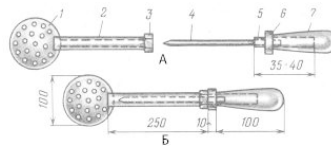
Черпак-пешня: 1 – черпак; 2 – трубка; 3 – гайка; 4 – стержень; 5 – болт; 6 – кольцо; 7 – ручка.
